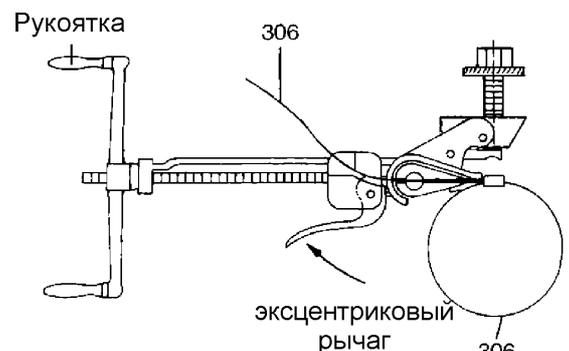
Затяжка шарнирного зажима с помощью зажимного инструмента Band-it и адаптера J050
